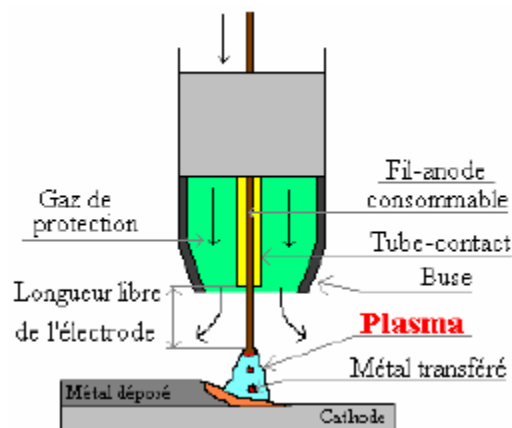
Schéma en coupe de l'extrémité d'une torche de soudage MIG-MAG [8].
